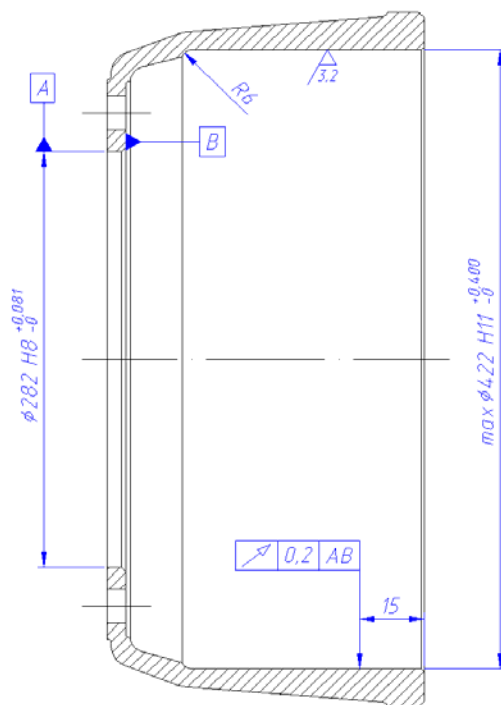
Размеры для обрабатывания барабана на токарном станке
